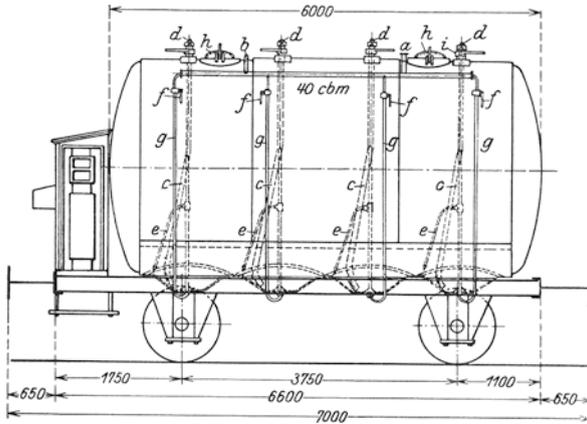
Braunkohlenstaubwagen mit liegenden Kesseln für 40 cbm Inhalt und 20 t Tragfähigkeit mit Preßluftantrieb, Bauart Gooßens, Längsschnitt.
